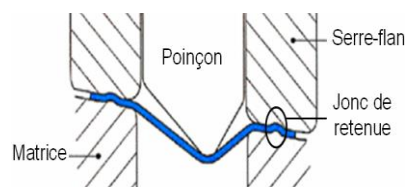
Procédé d'emboutissage avec freinage de la tôle sous serre-flan.
